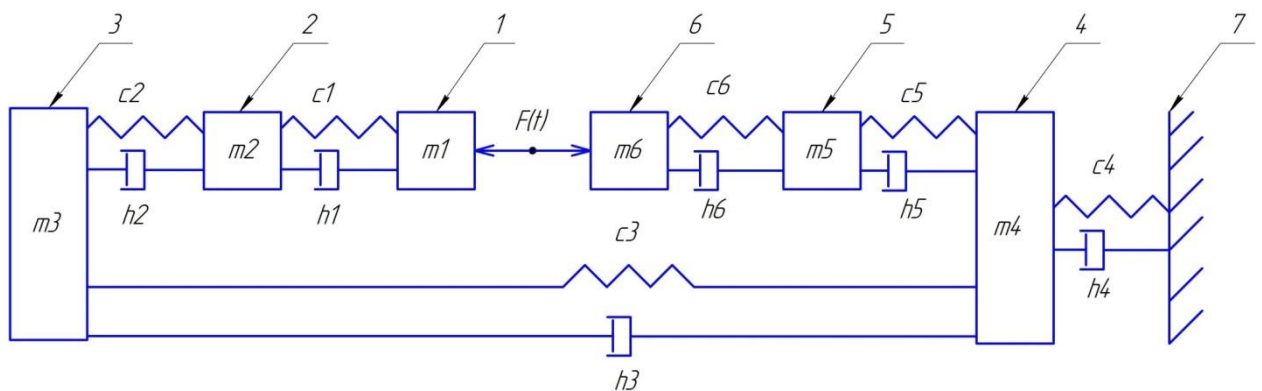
Расчетная схема. 1. Заготовка; 2. Токарный патрон; 3. Передняя бабка; 4. Станина; 5. Суппорт; 6. Инструментарий.
